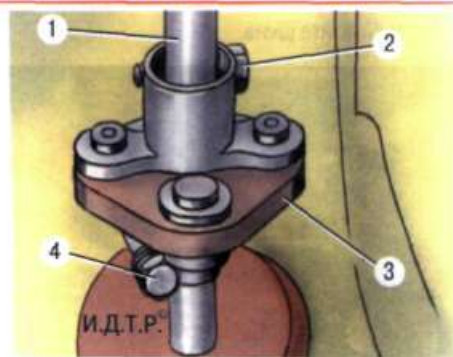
Муфта вала рулевого колеса: 1 – вал рулевого колеса; 2 – верхний стяжной болт; 3 – муфта; 4 – нижний стяжной болт
